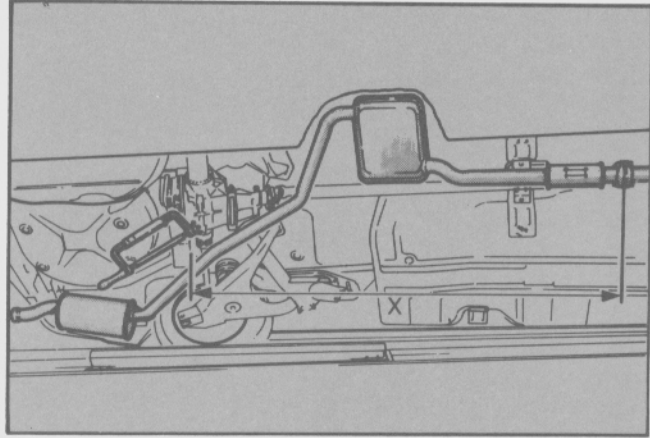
Zonas de corte. Dimensión x = 1.635 mm; y = 2.117 mm.
